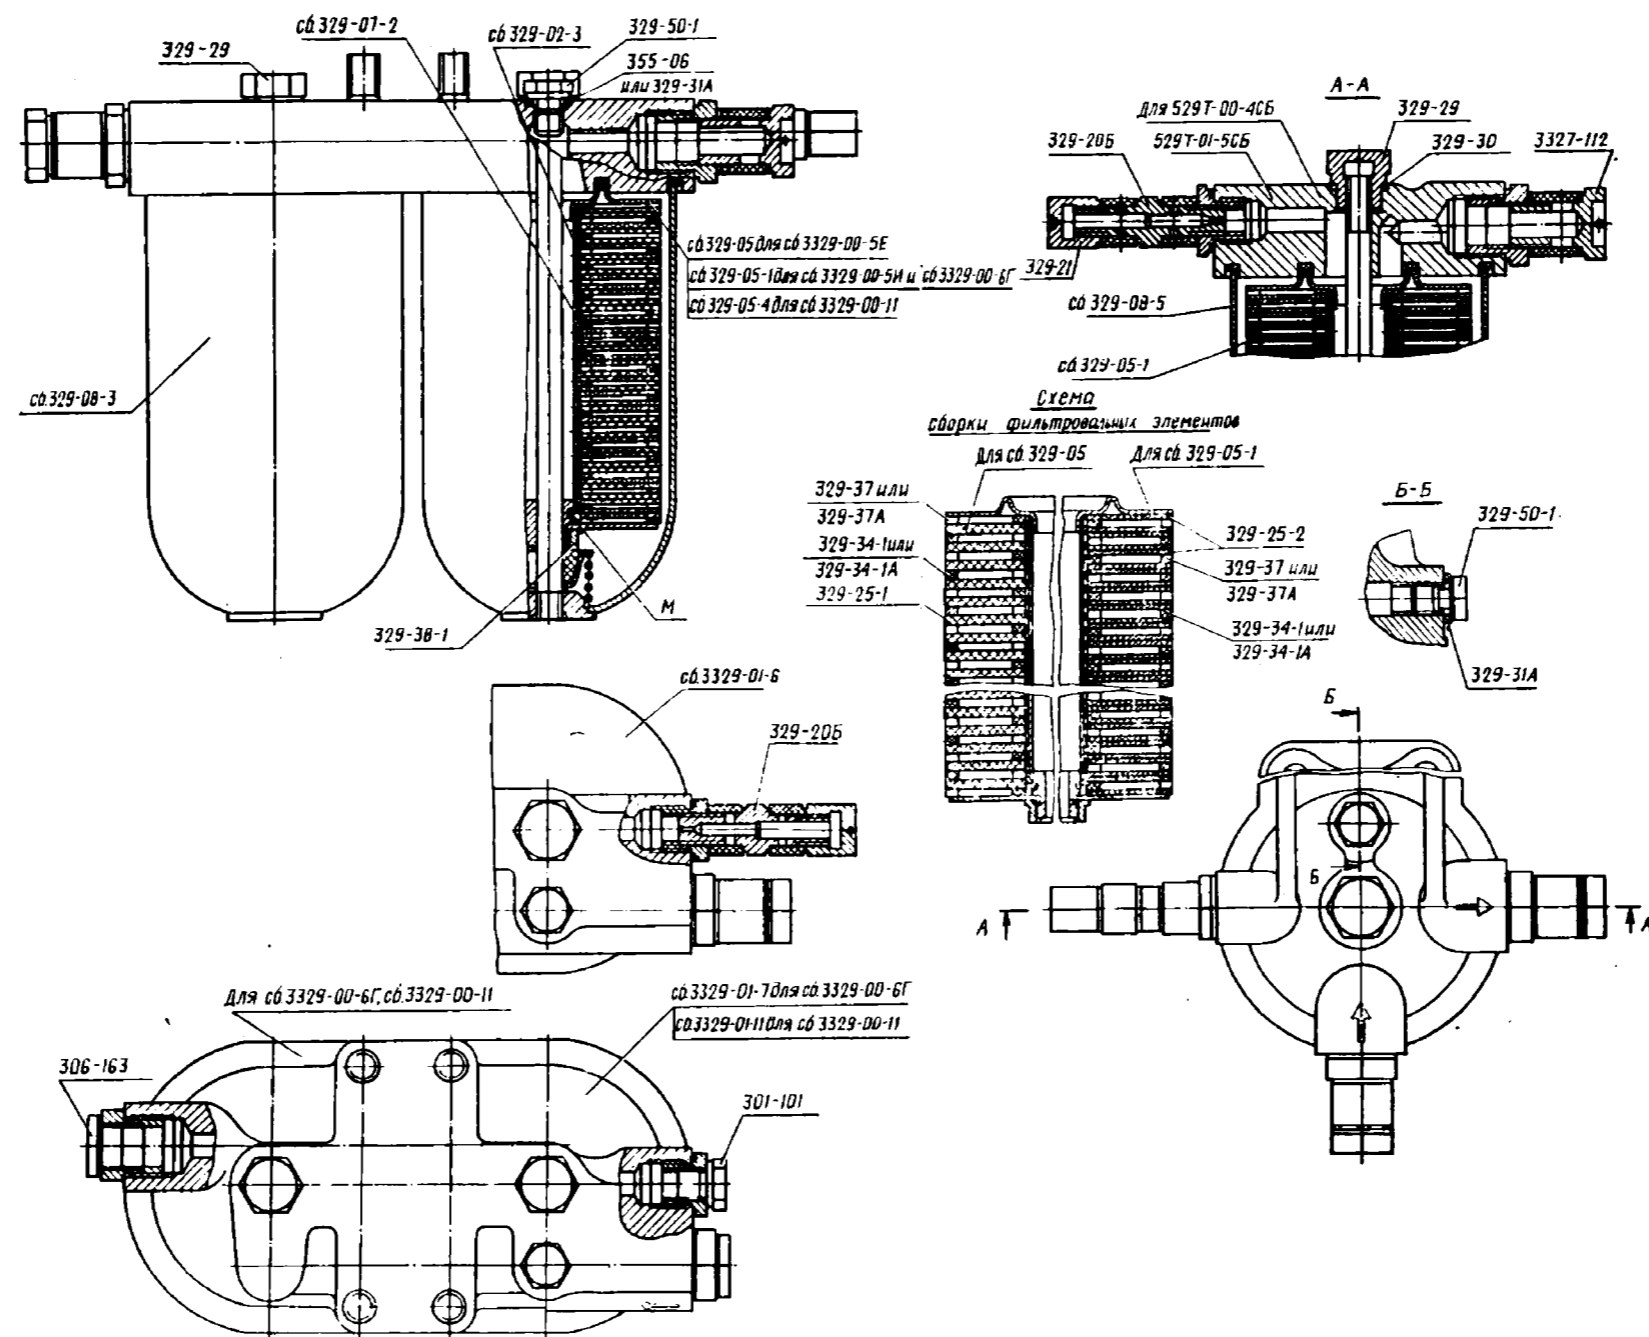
Фильтр топливный сб.3329-00-5И, сб.3329-00-5Е, сб.3329-00-6Г, сб.3329-00-11 и 529Т-00-4СБ:
